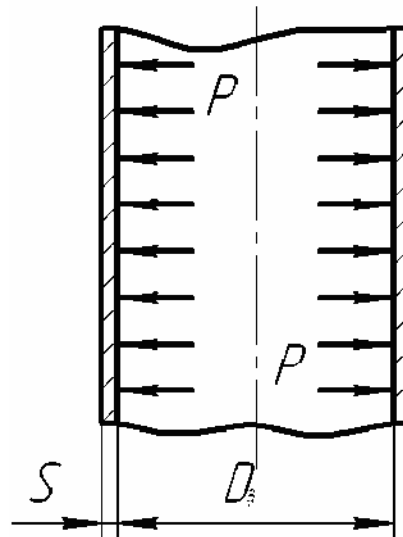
Розрахункова схема циліндричної обичайки
